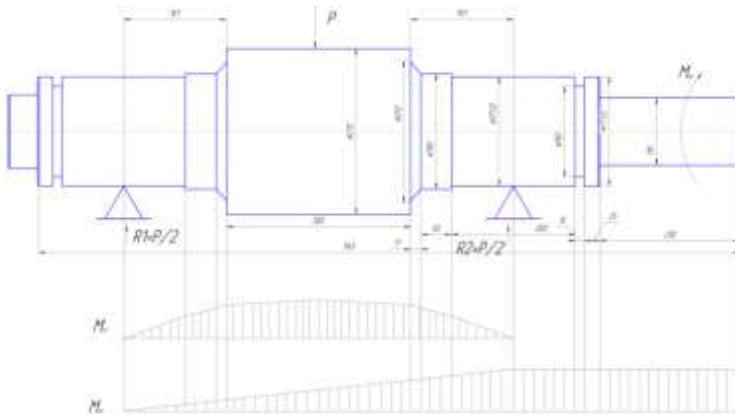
Расчетная схема валка под нагрузкой, эпюры изгибающего и крутящего моментов
